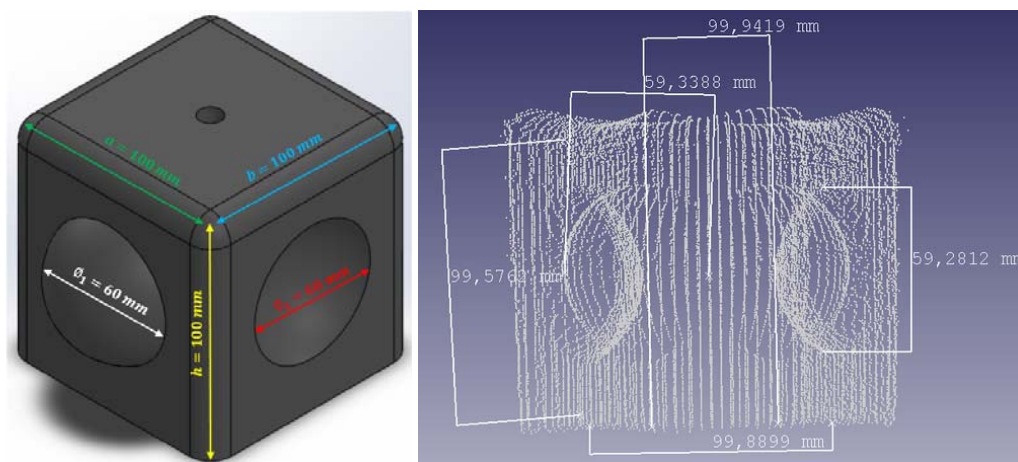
Prueba dimensional del objeto cóncavo-convexo: Diseño CAD (Izq.) y Nube de puntos (Der.)
